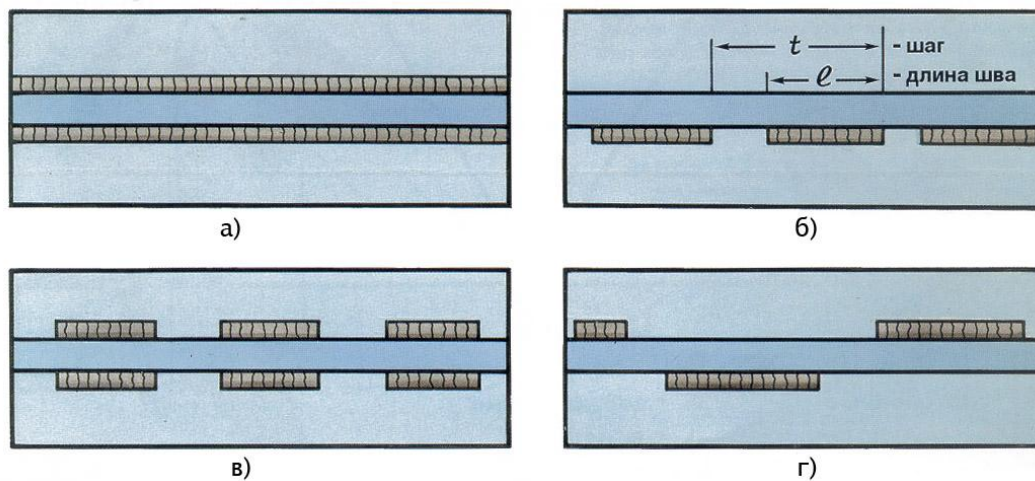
Виды сварных швов по протяженности: а – непрерывный, б – цепной односторонний, в – цепной двухсторонний, г – шахматный;  $l$  – длина шва,  $t$  – шаг шва
